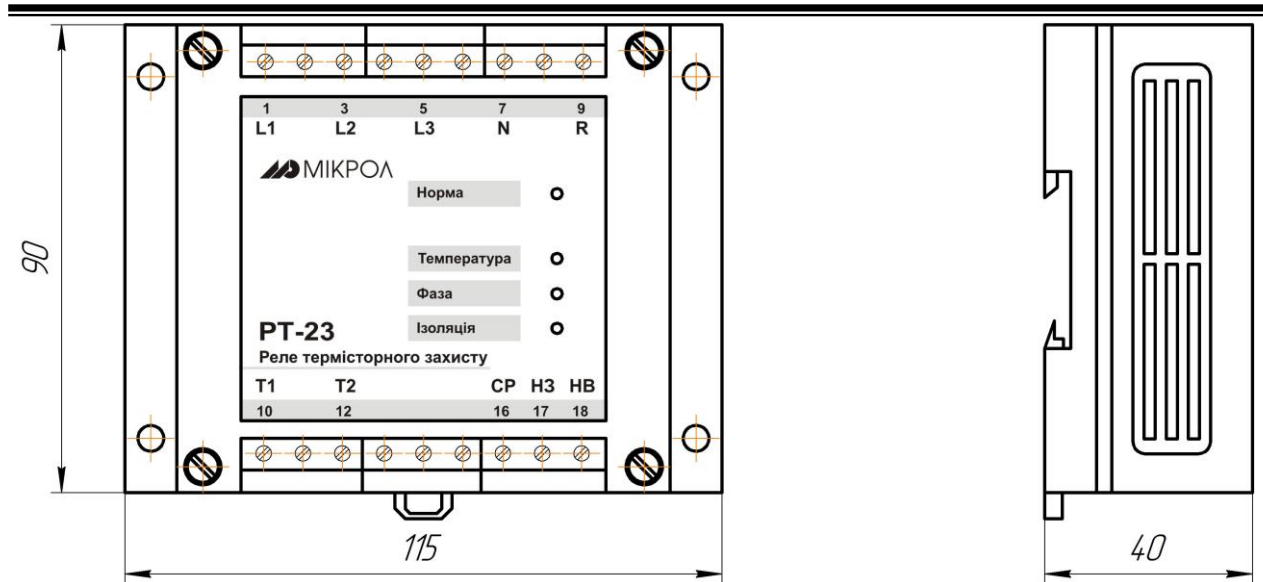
Внешний вид и габаритные размеры РТ-23
